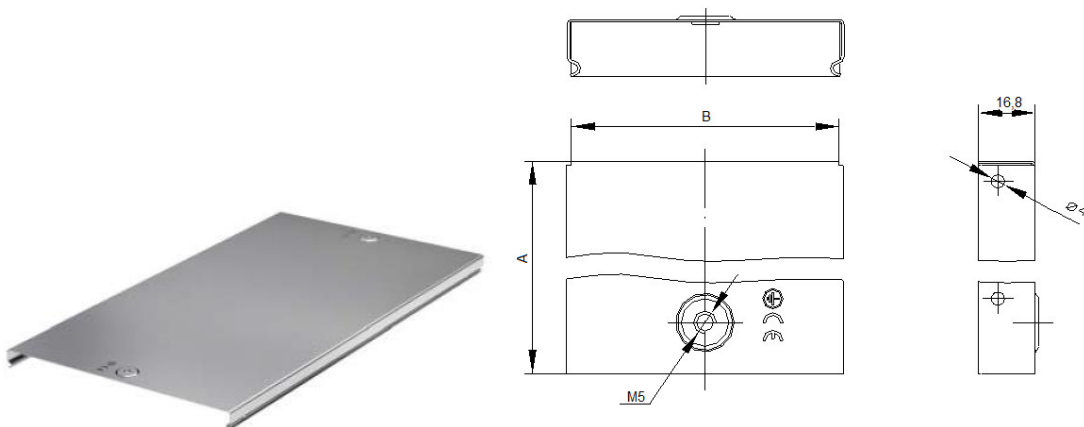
Крышка CDV 90 на угол вертикальный внешний, тип 3834
